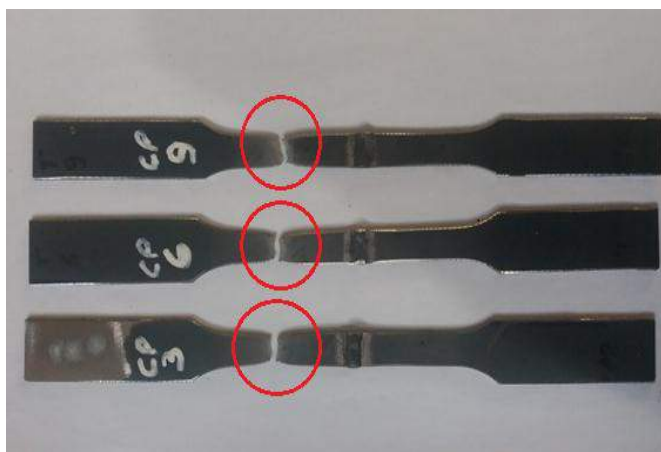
Corpos de prova do material soldado de topo com a estrição em destaque
